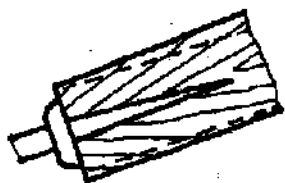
Вставка хвостовика стамески в заготовку рукоятки
